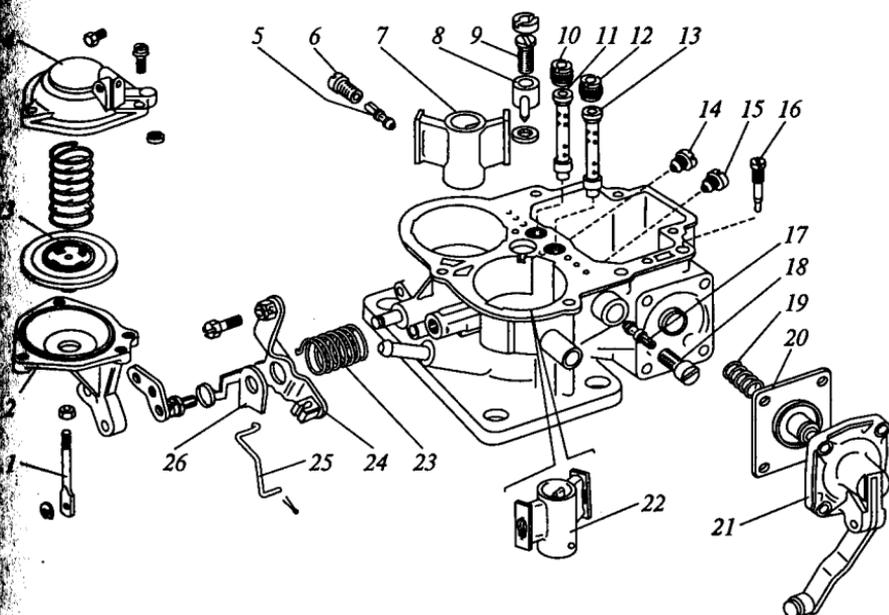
Детали корпуса карбюратора 2105-1107010:
